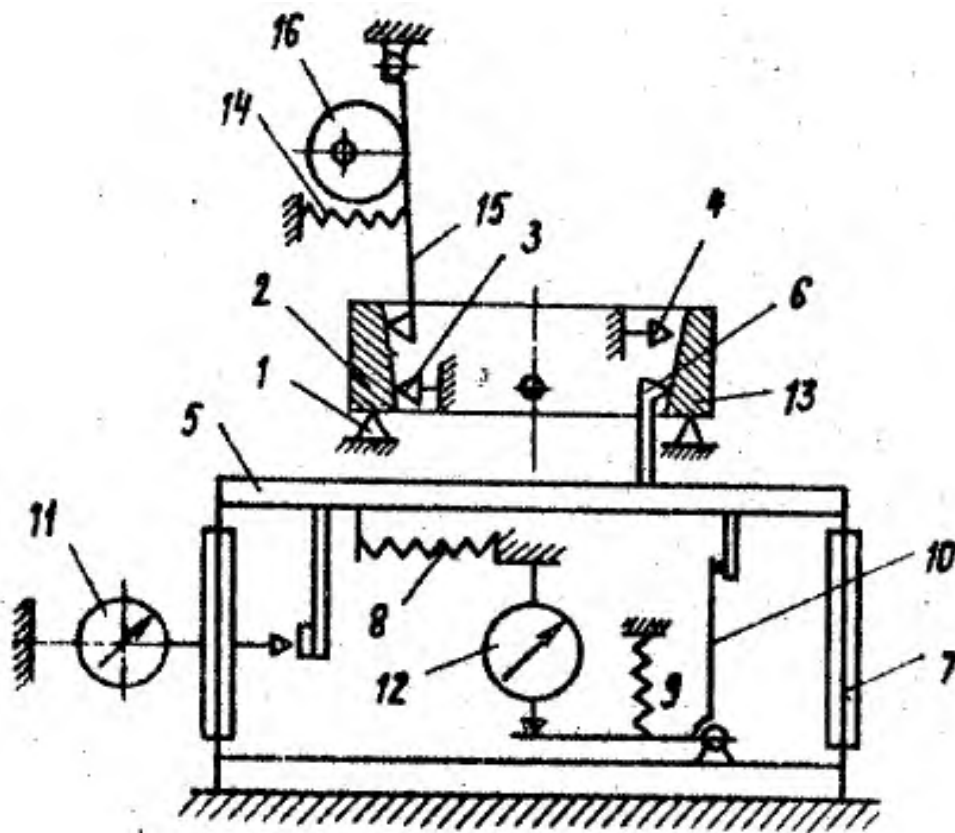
Пристрій для вимірювання внутрішнього конуса та діаметра зовнішніх кілець конічних підшипників
